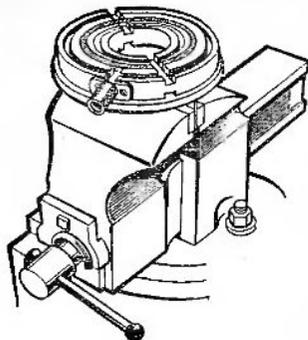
Приспособление для шлифования стыков поршневых колец и подгонки колец по высоте.
